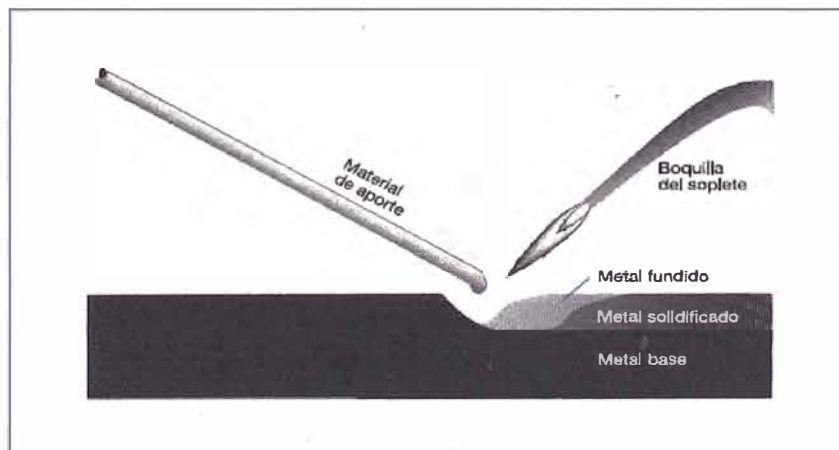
Esquema Proceso OFW (Fuente: Manual de Soldadura Indura)
